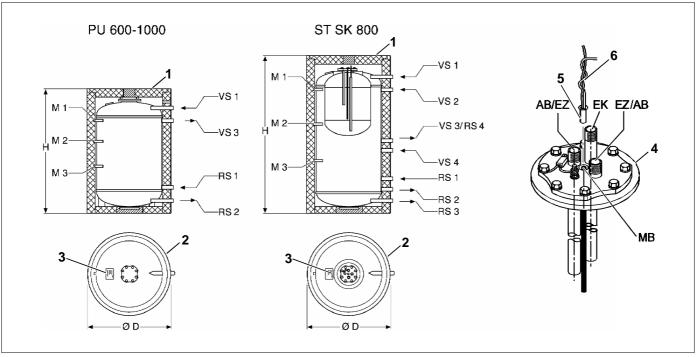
Dimensioni ed attacchi (vista frontale e da sopra)
